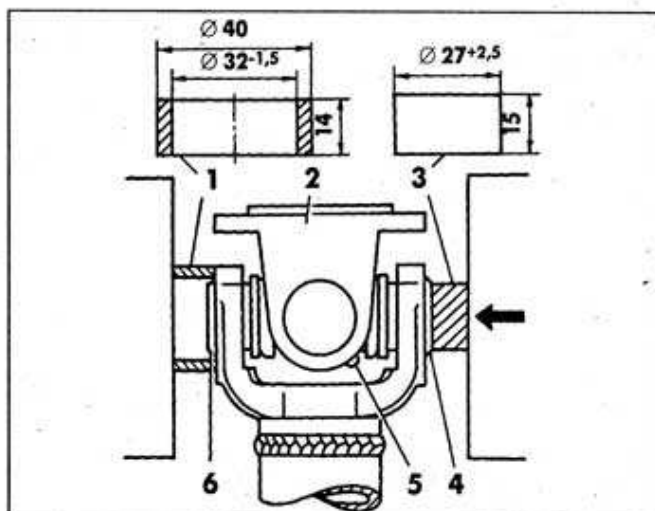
Разборка карданного шарнира: 1 – кольцо; 2 – фланец шарнира; 3 – оправка; 4, 6 – подшипники; 5 – пресс-масленка
